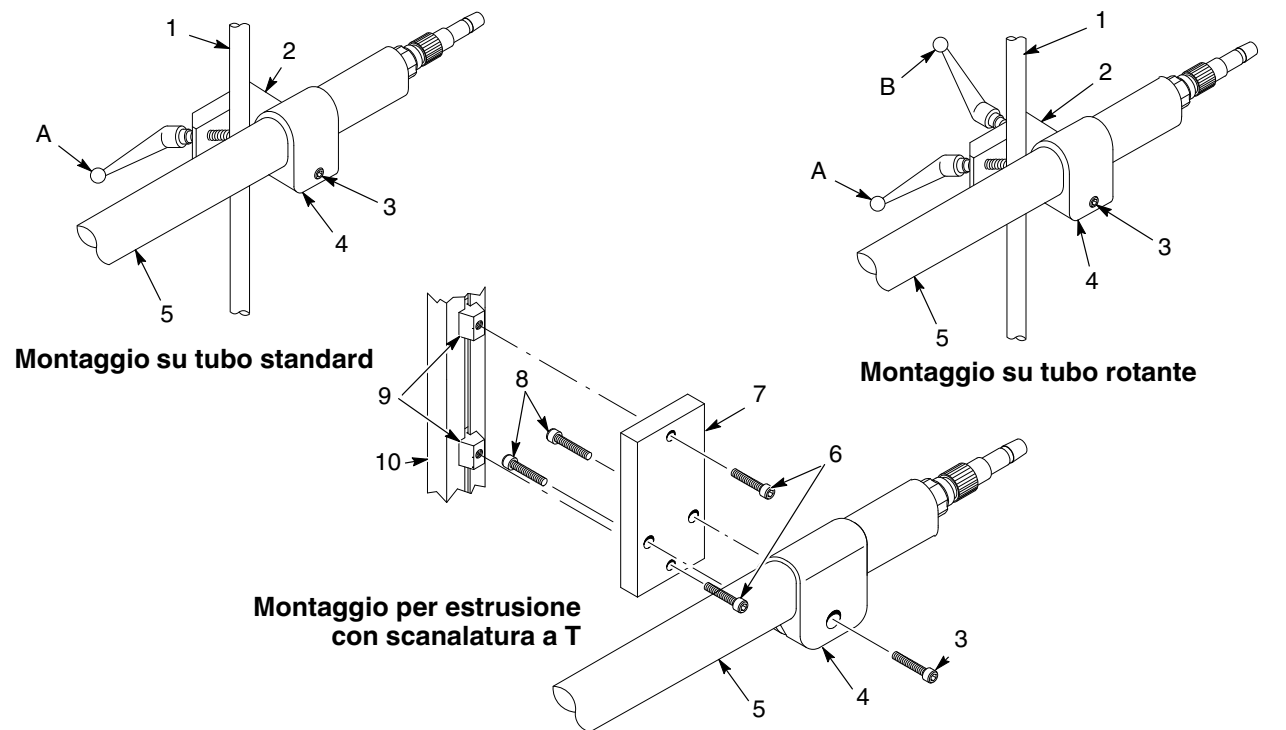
Gruppi di montaggio della pistola con montaggio su tubo
